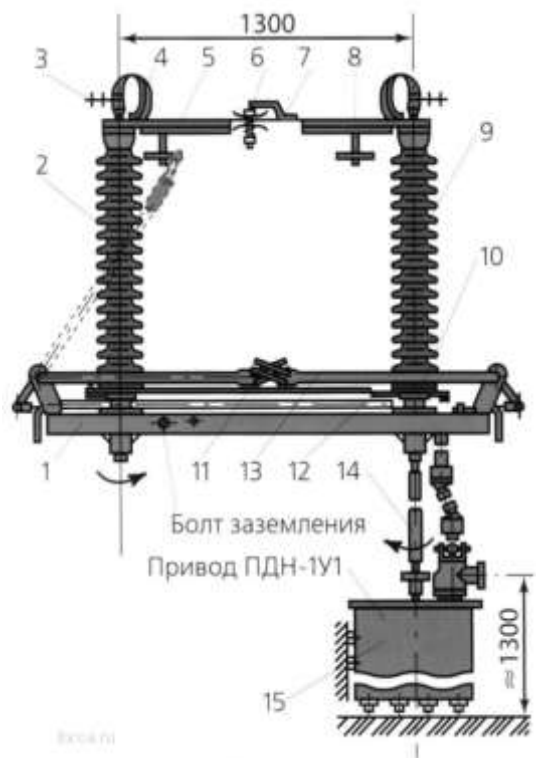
Установка роз'єднувача на залізобетонній опорі:
